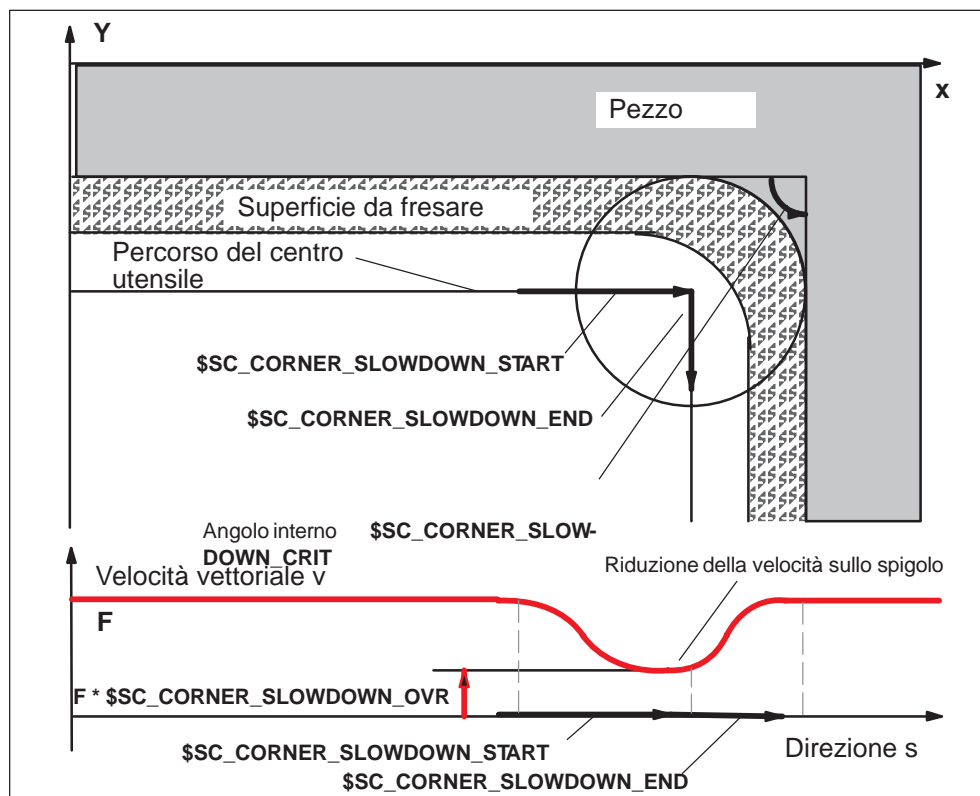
Parametrizzazione della riduzione dell'avanzamento G62 riportata nell'esempio di uno spigolo di 90°
